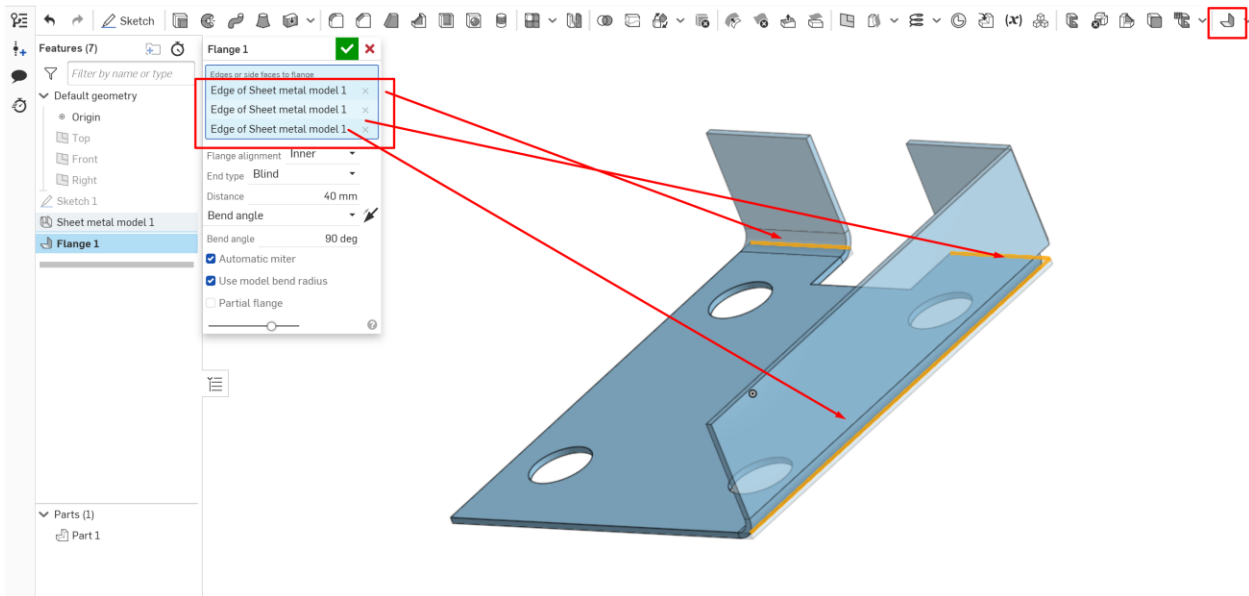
Формування конфігурації за допомогою інструменту FLANGE
